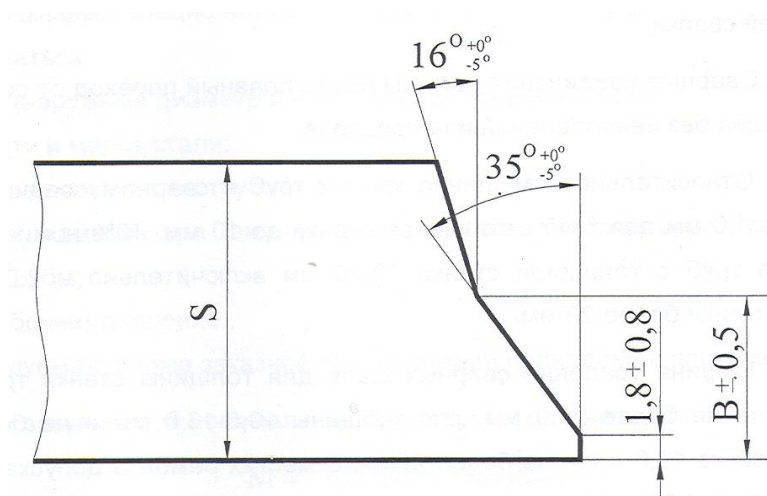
Разделка кромок под сварку при толщине стенки более 15 мм
